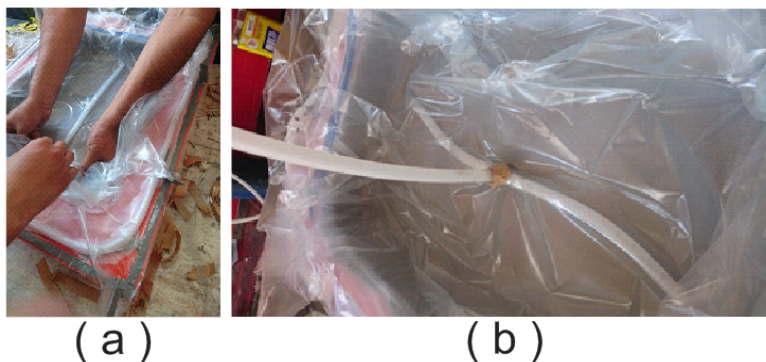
(a) Acomodo de la bolsa de vacío sobre el molde. (b) Pieza a punto de ser impregnada con resina.
